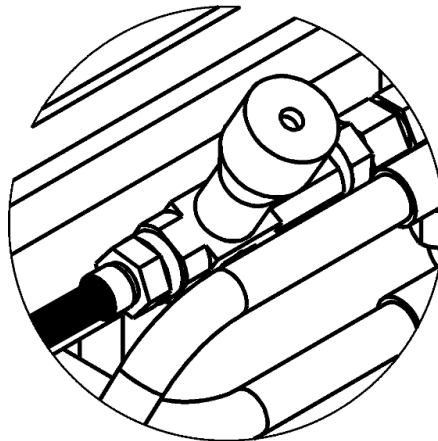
Обратный дроссельный клапан обрезчика пленки
